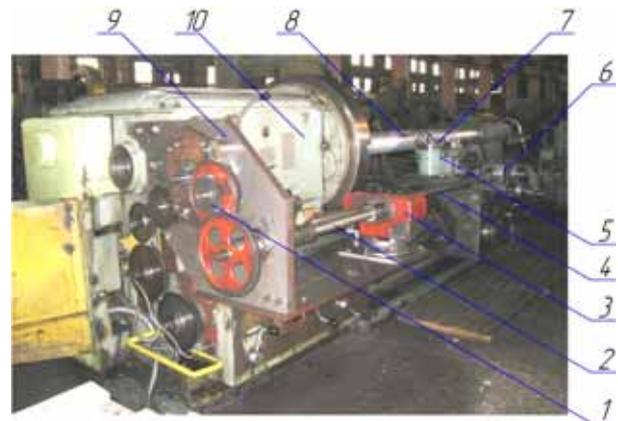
Общий вид опытного устройства: 1 – гитара сменных зубчатых колес; 2 – вал; 3 – раздаточная коробка; 4 – ходовой вал; 5 – шпиндельная головка; 6 – конический редуктор; 7 – многолезвийный инструмент; 8 – обрабатываемая заготовка; 9 – механизм круговой подачи; 10 – станок 1М65
